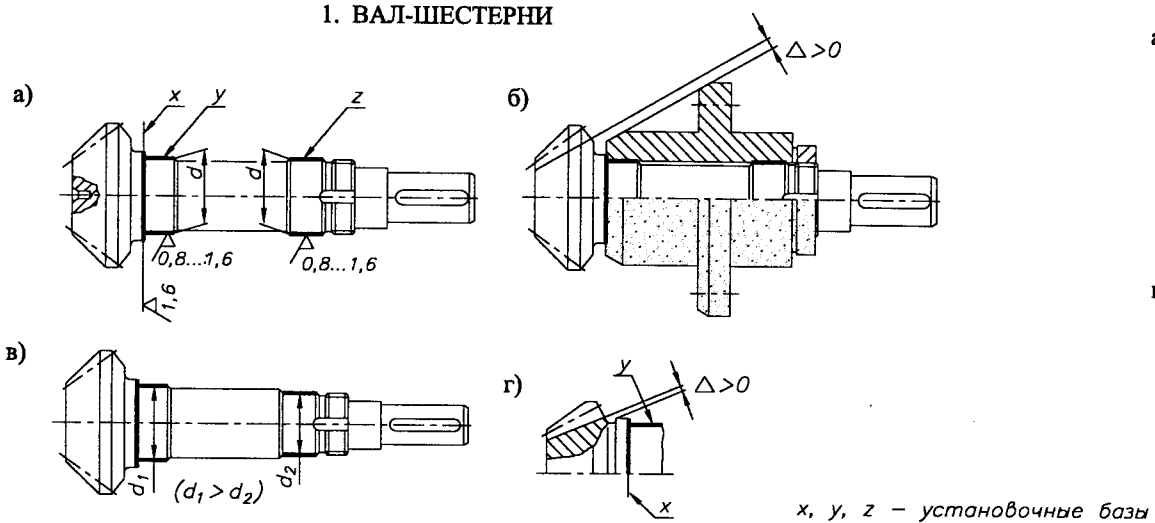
Установочные базы для нарезания зубьев на вал-шестернях
